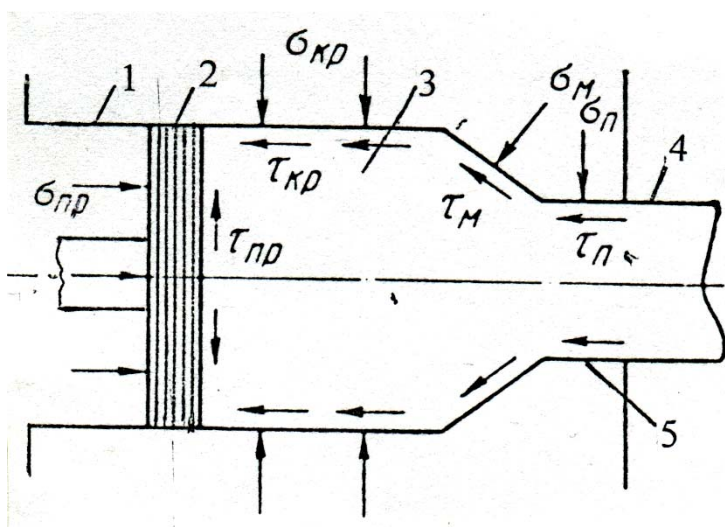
Схема напружень, що діють на метал в процесі пресування: 1 - контейнер; 2 - прес-шайба; 3 - заготовка; 4 - профіль; 5 - поясок.
